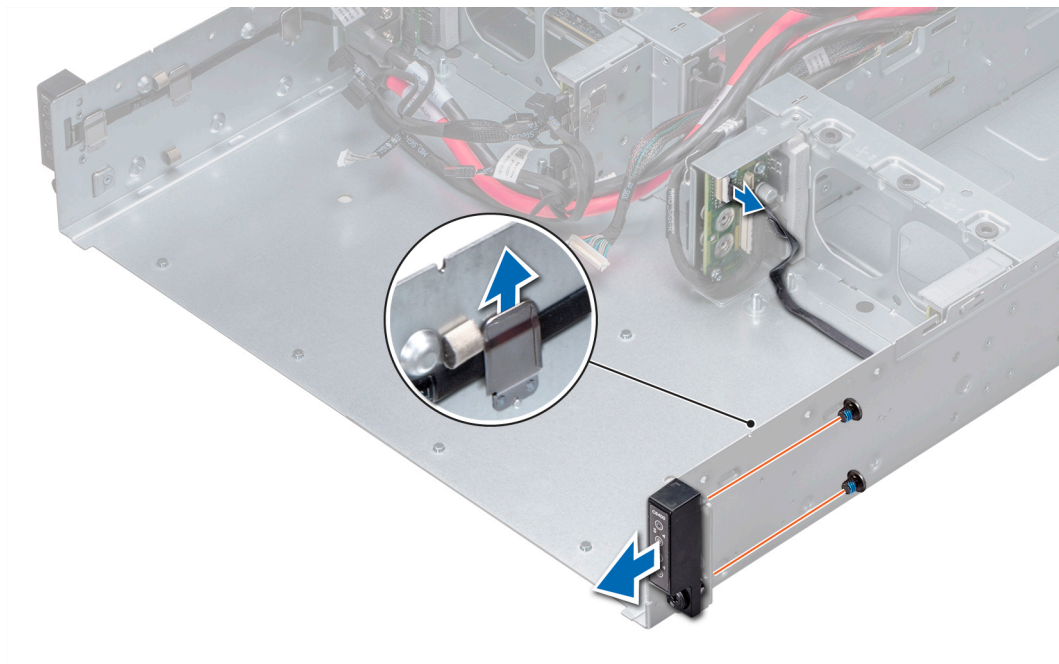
Entfernen der rechten Bedienfeldbaugruppe
